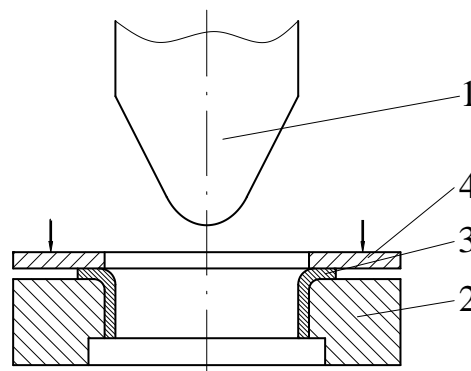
Схема розбортовування (розвальцювання):
